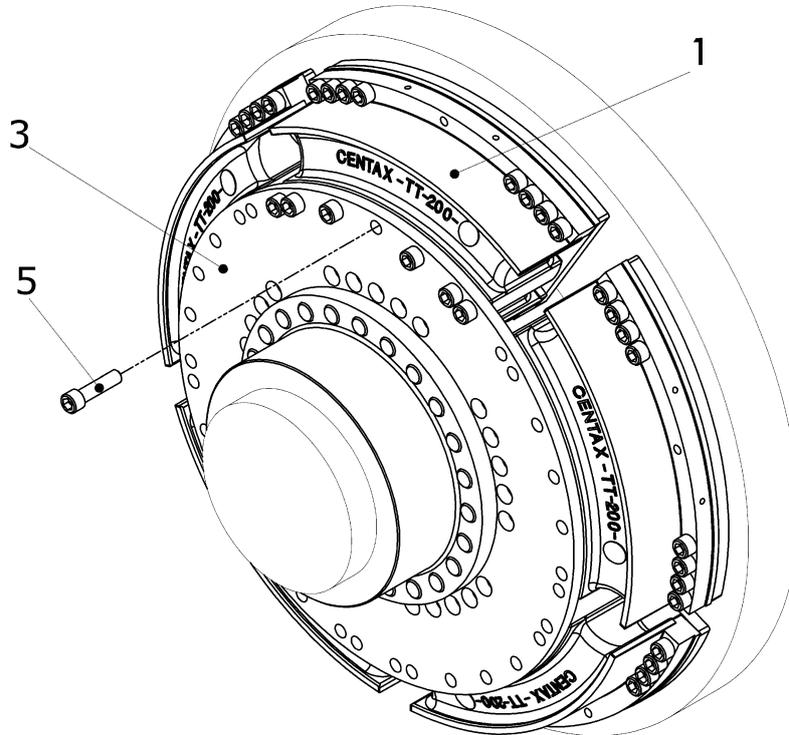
Adapter (3) mit Gummielementen verschrauben
